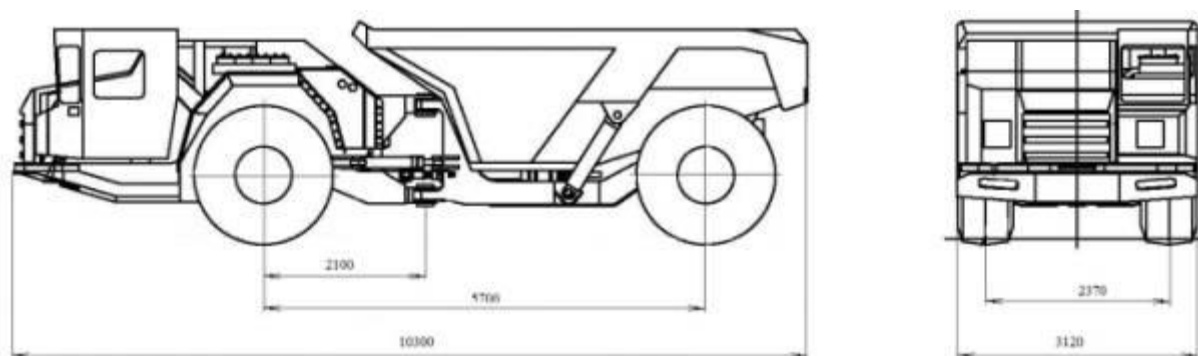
Габаритные размеры самосвала БелАЗ-75800
